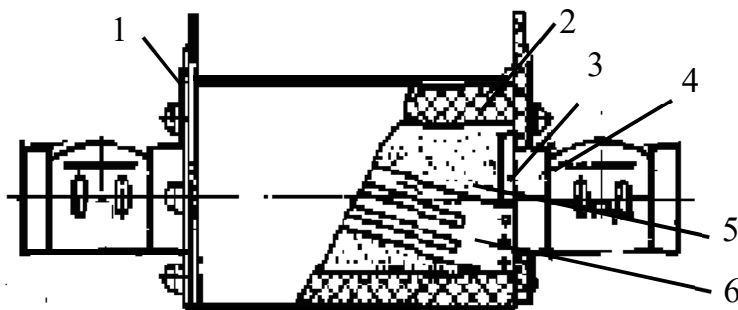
Плавкий запобіжник типу ПН2
